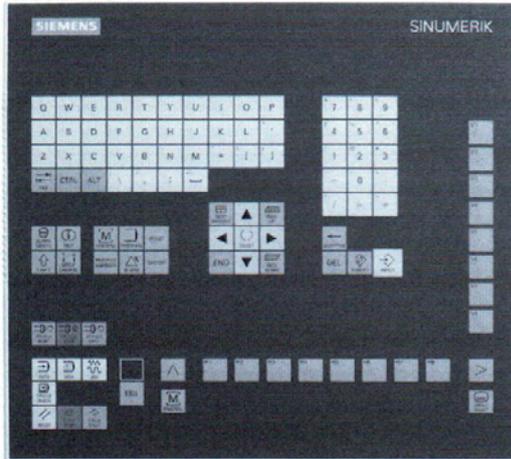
Tastatur einer CNC-Maschine (Beispiel Siemens AG)
